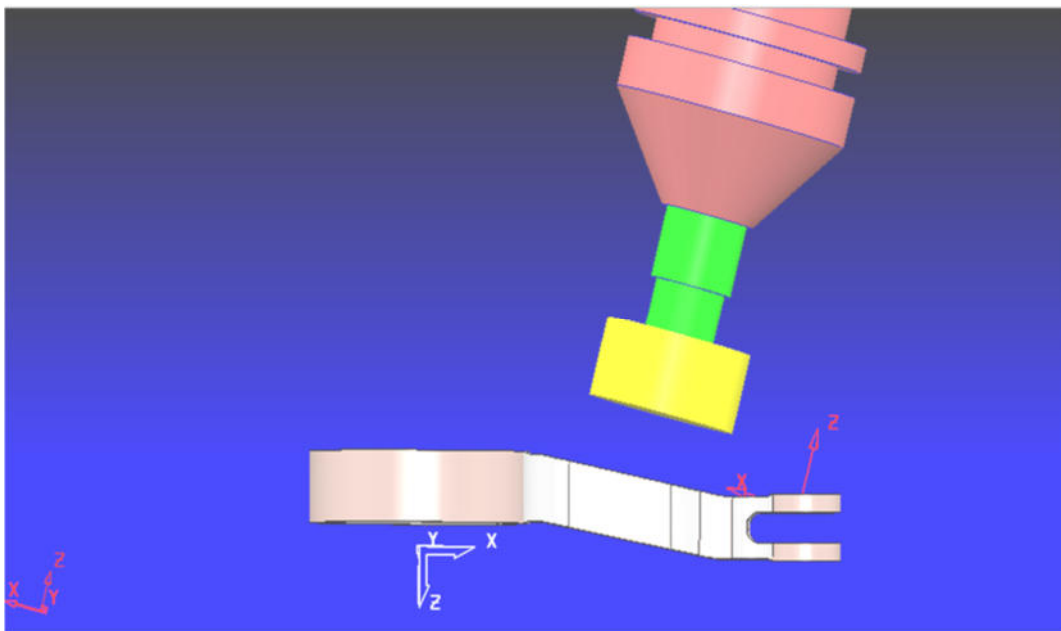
Фрезерування торцевою фрезою поверхні - 3,
